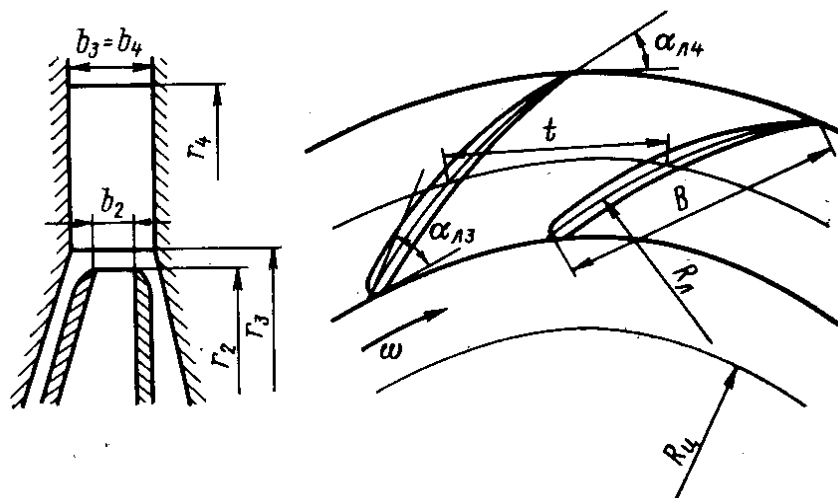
Схема кругової решітки лопаткового дифузора
